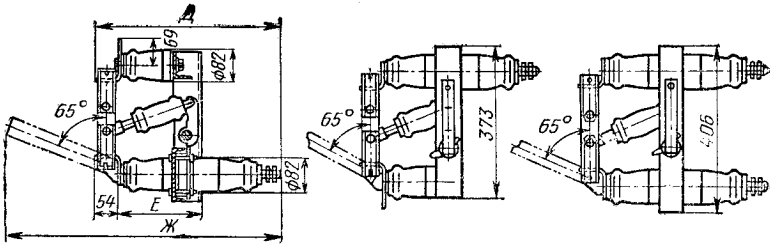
Разъединитель РВФ. Исполнения II, III, IV.
